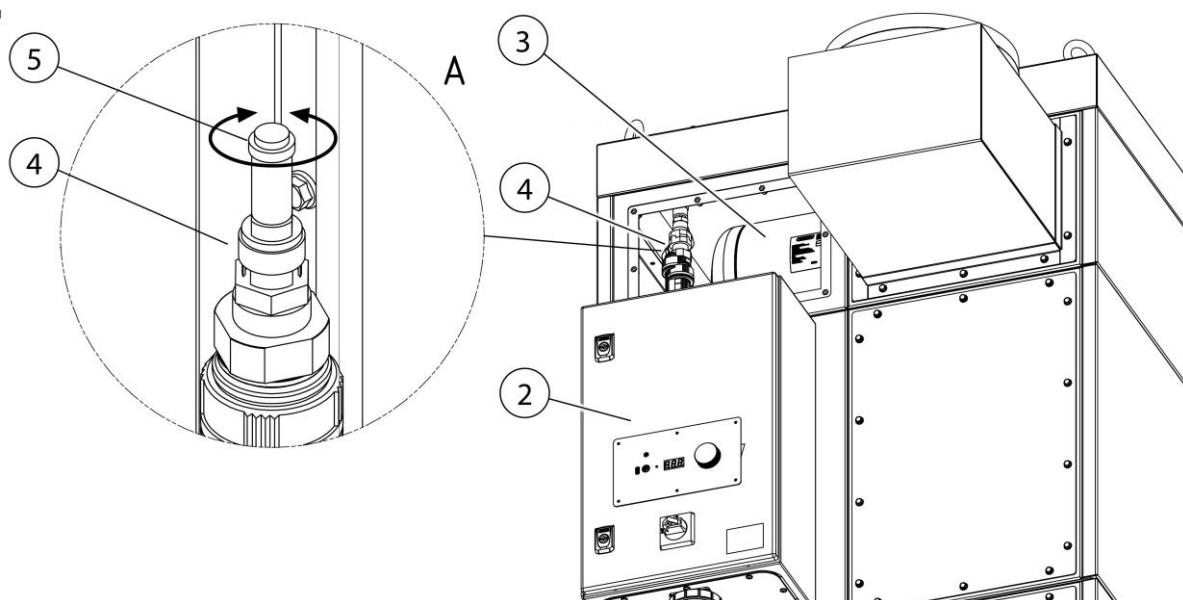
Проверка предохранительного клапана сжатого воздуха
